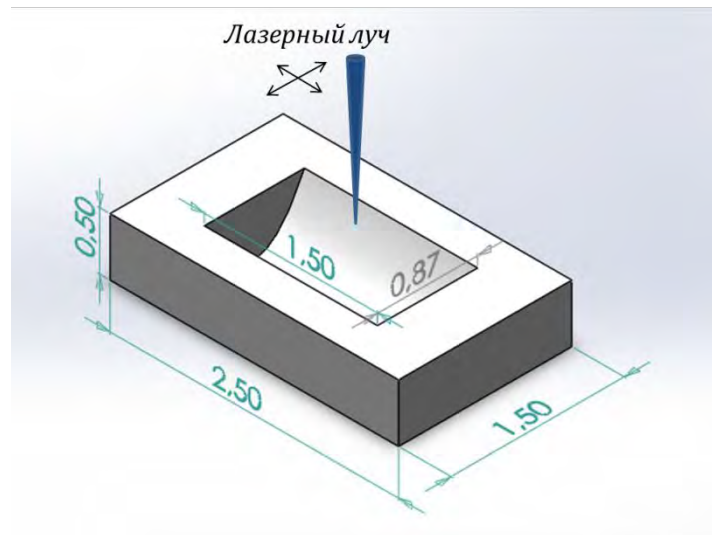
Схематический чертеж одномерной одиночной преломляющей алмазной полу-линзы. Размеры указаны в миллиметрах. Показаны направления падения и движения лазерного луча.
